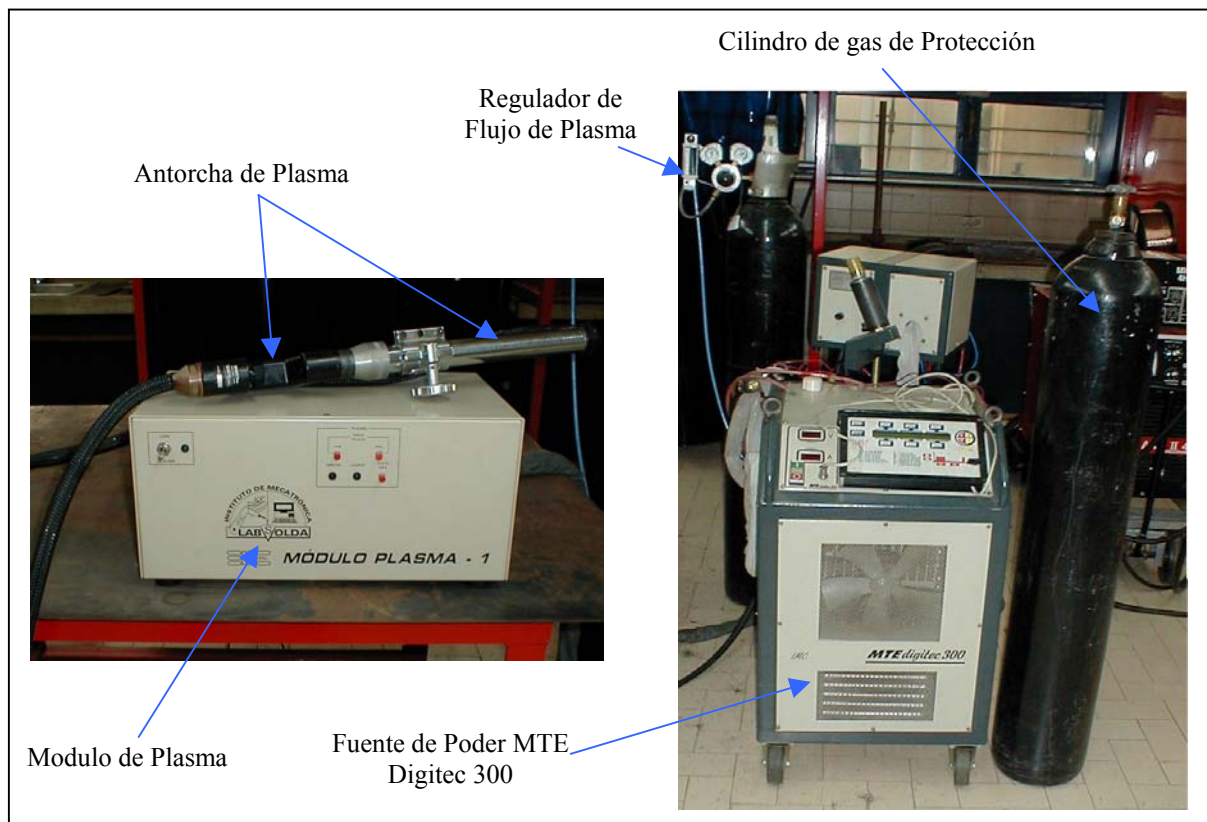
Equipo típico para soldadura por arco de plasma (PAW).
